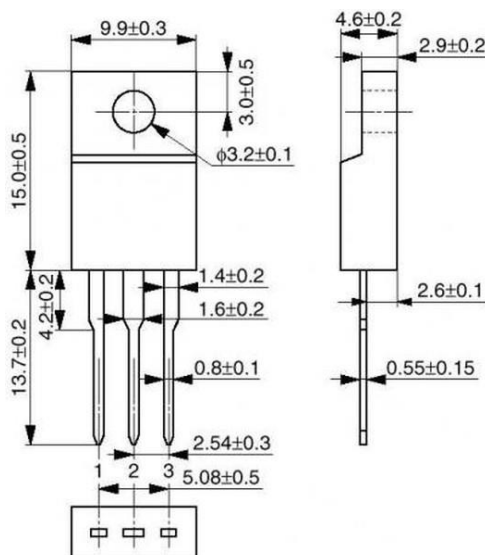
Габаритні розміри мікросхеми MC7805
